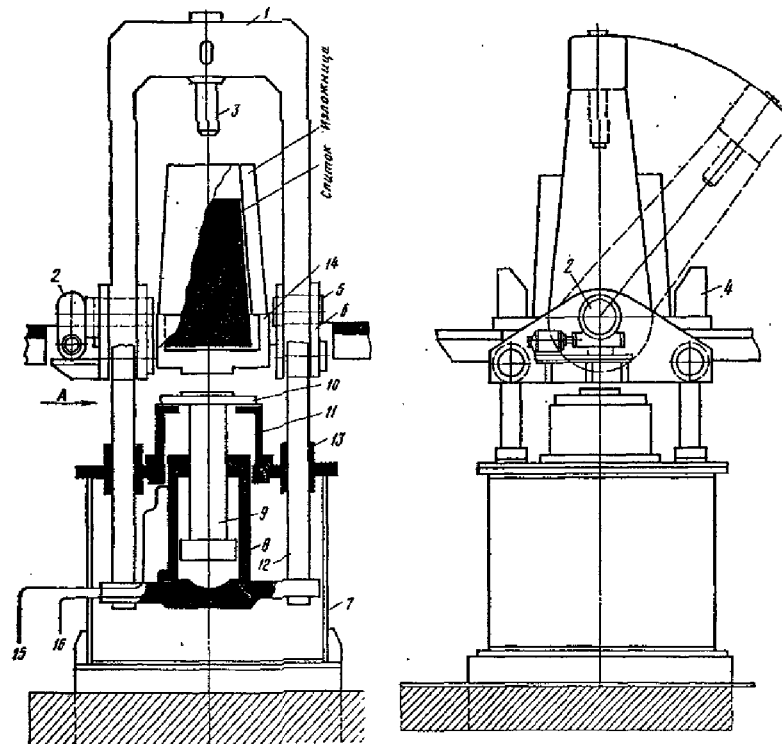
Пристрій для виштовхування злитка з виливниці
